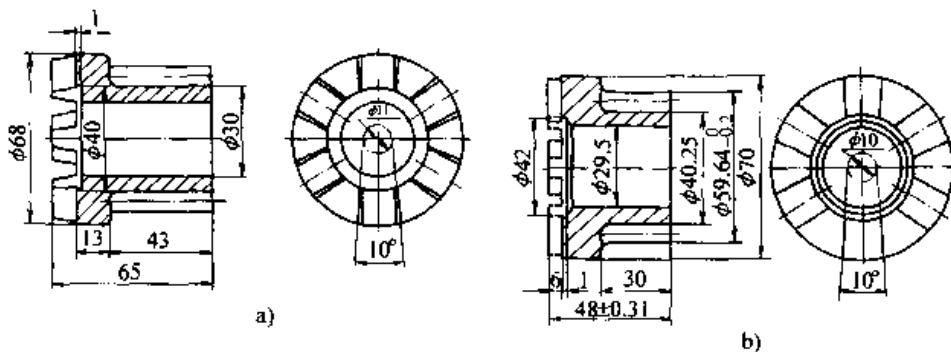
圆柱齿轮粉锻毛坯图和锻件图
